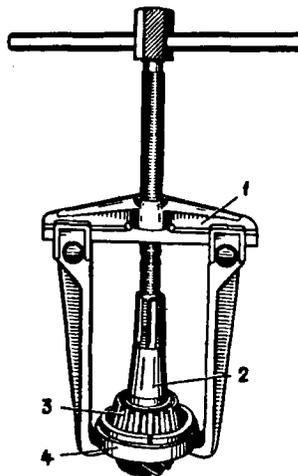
Снятие внутреннего кольца заднего подшипника ведущей шестерни универсальным съемником А.40005/1/7: 1 - универсальный съемник А.40005/1/7; 2 - ведущая шестерня; 3 - внутреннее кольцо подшипника; 4 - приспособление А.45008
